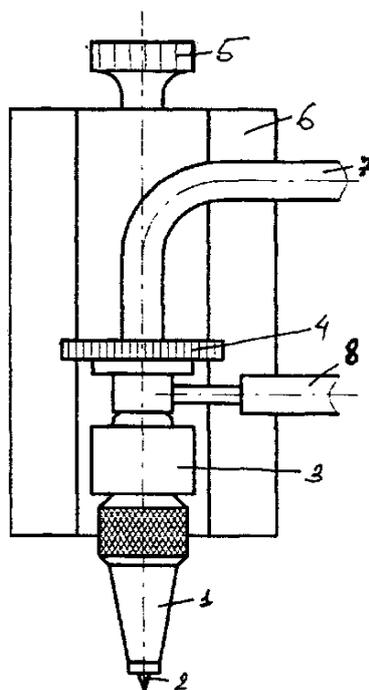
Устройство малогабаритной сварочной горелки
